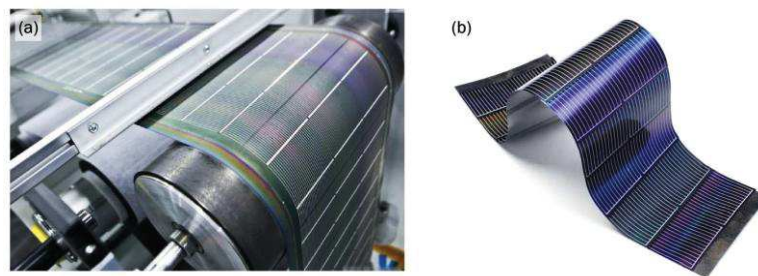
a) Fabrication de cellules en couches minces par procédé roll-to-roll.
